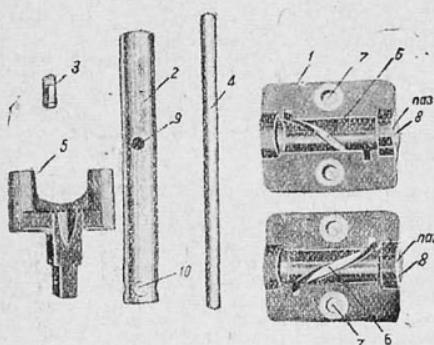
Детали приспособления для нарезки смазочных канавок. Справа показаны шаблоны приспособления
